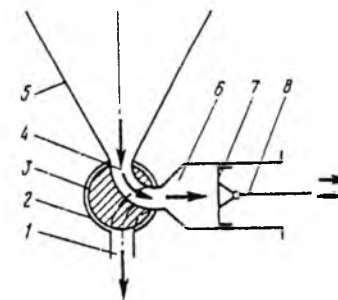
Схема дозатора для вязких жидкостей: 1 — патрубок; 2 — камера; 3 — отсекающий элемент; 4 — криволинейное отверстие; 5 — бункер; 6 — дозирующий цилиндр; 7 — поршень; 8 — шатун
